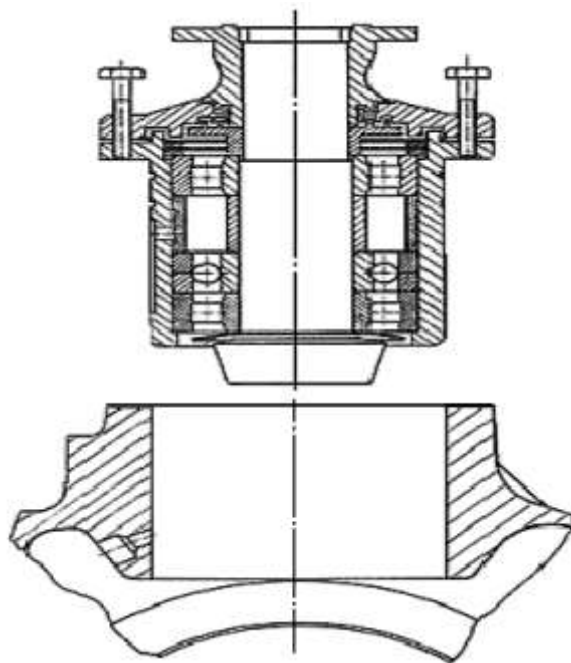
Разборка узла ведомого вала
